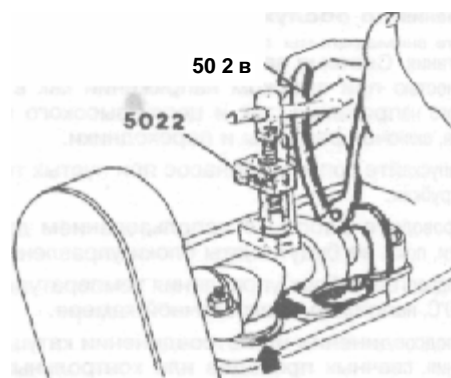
Установка приспособления 5022 и удаление диска — двигатели B230F и B230FT
